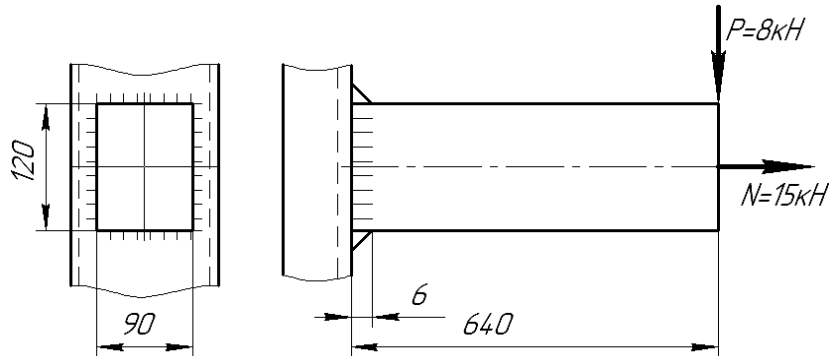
Сварное соединение бруска со швеллером
